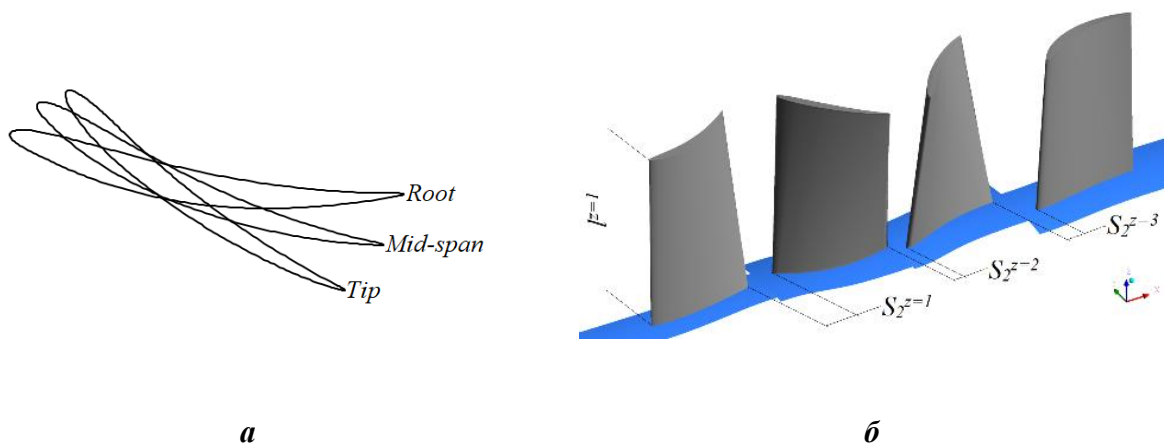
Построение лопатки (а) и проточной части (б) осевого компрессора
